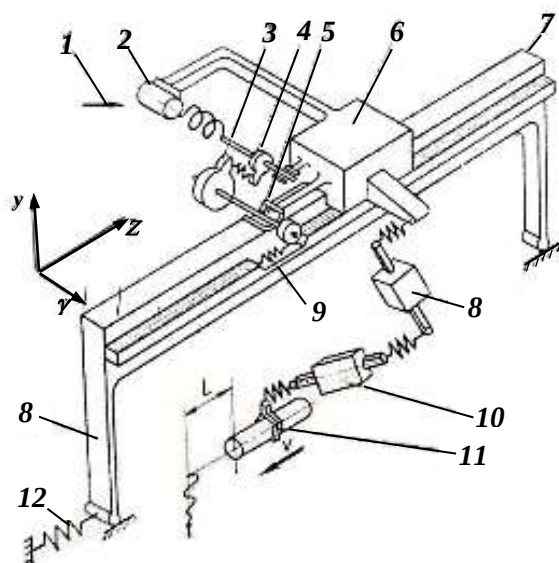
Модель продольного (транспортного) перемещения ПР мод. ЦРБ-50:1-сигнал управления; 2-двигатель; 3и 4зубчатые колеса; 5-корпус вала; 6-тележка; 7-монорельс; 8-плечо руки; 9-зубчато – реечная передача; 10-предплечье руки; 11-схват с деталью; 12-жесткость опор монорельса; 13-опора монорельса; X, Y, Z- оси координат; L- продольное перемещение схвата вдоль оси Z; v-скорость продольного перемещения схвата.
